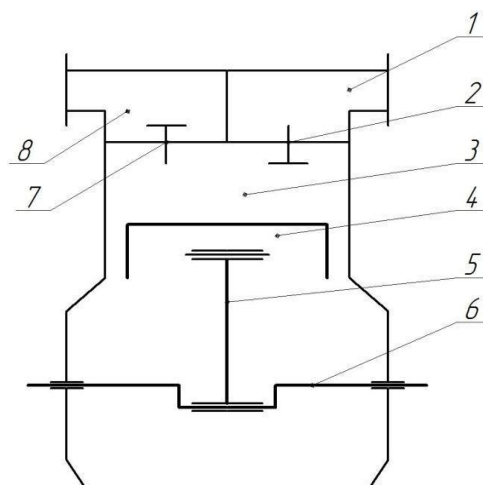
Схема поршневого компрессора с одной рабочей камерой и тронковым поршнем
